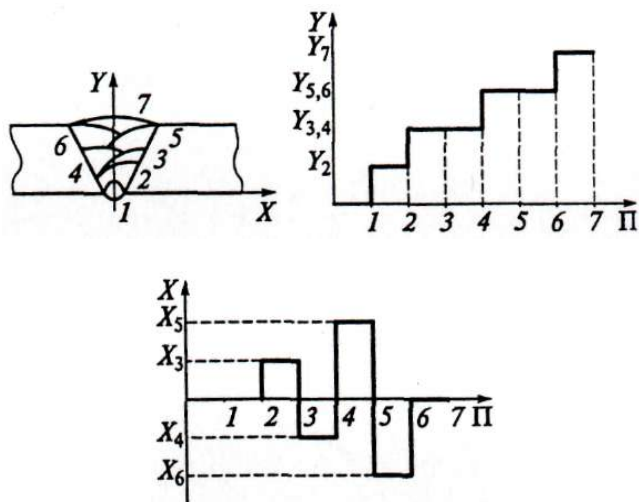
Схемы заполнения разделки стыка (а) и перемещения (П) сварочной горелки по координатам  $X$ (б) и  $Y$ (в) при многослойной сварке: 1–7 – номера проходов при сварке
